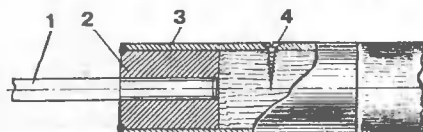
Резьбовое соединение рыхлителя с ручкой:
